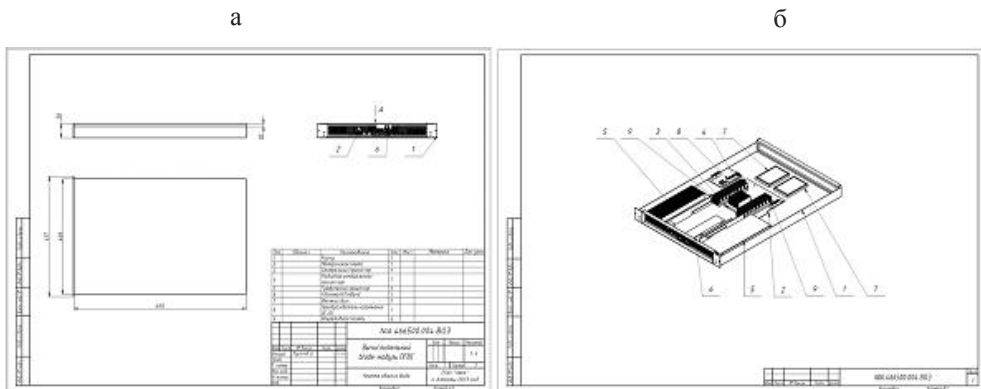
Чертеж общего вида вычислительного blade-модуля ПГВС:
